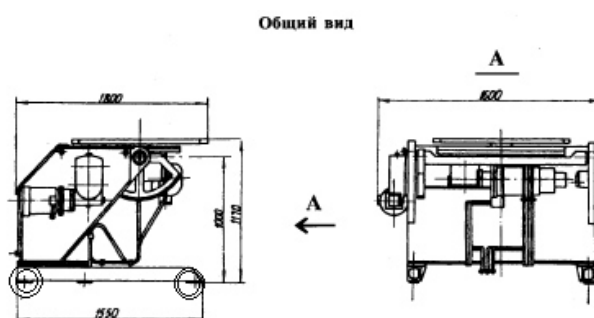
Вращатель сварочный универсальный РТ-3000
